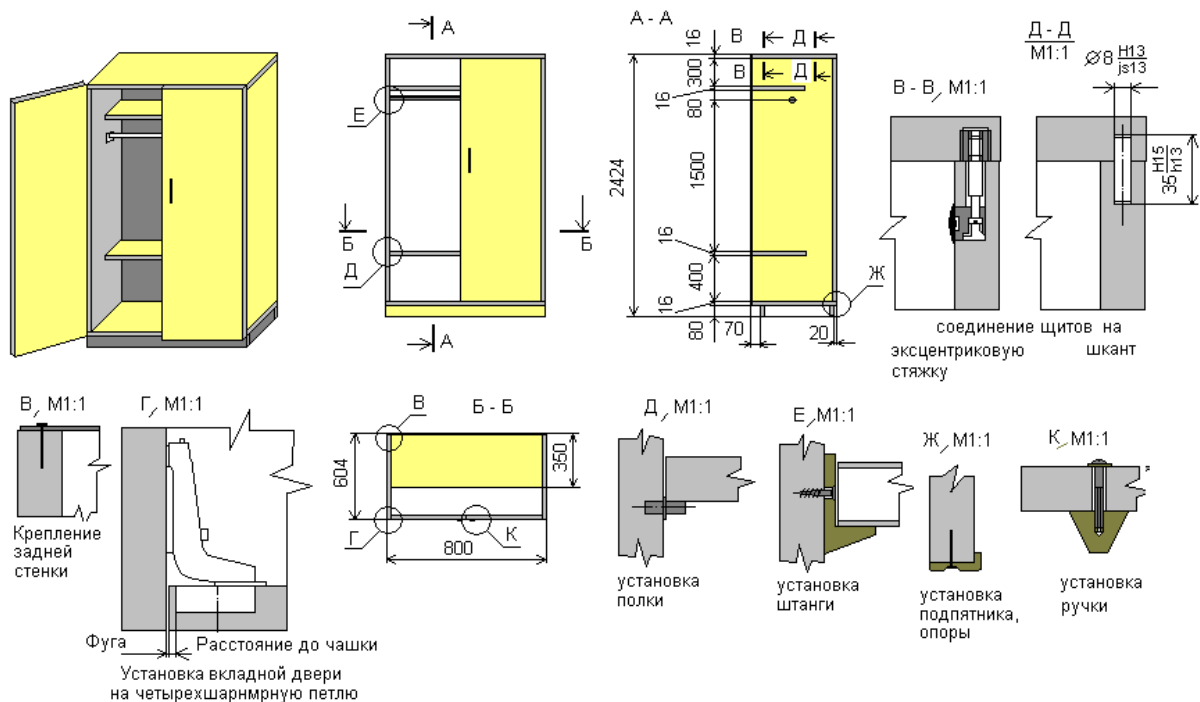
Общий вид и сборочный чертеж шкафа для одежды
